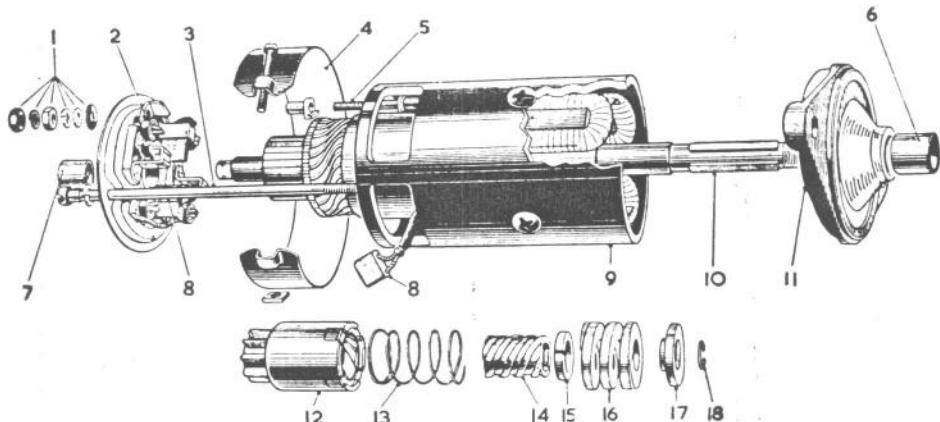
Despiece del motor de arranque. Lucas.
